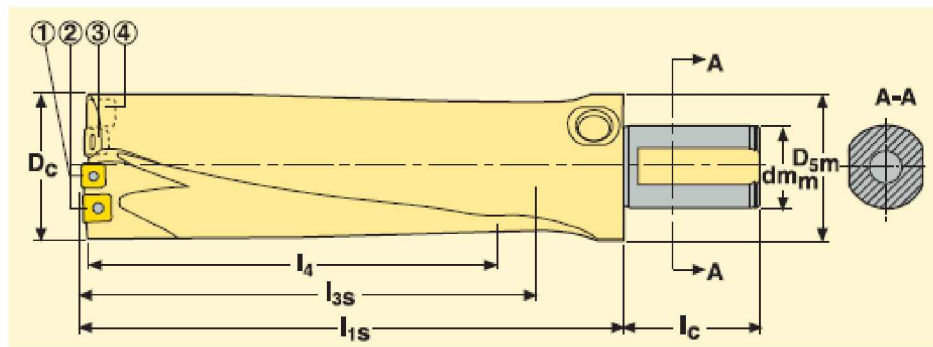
Корпус SD542-60-150-40R7 [2, с. 139]
